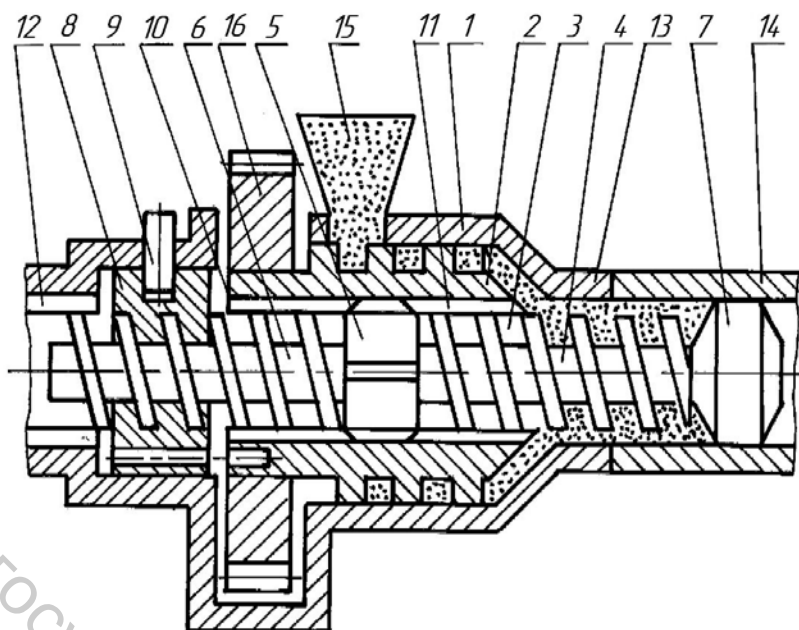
Схема нанесения внутренних покрытий с развитой поверхностью
